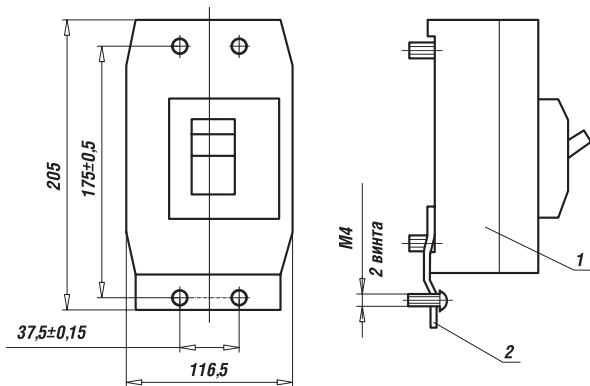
Установочные размеры выключателя для крепления на рейках с закрытым пазом
